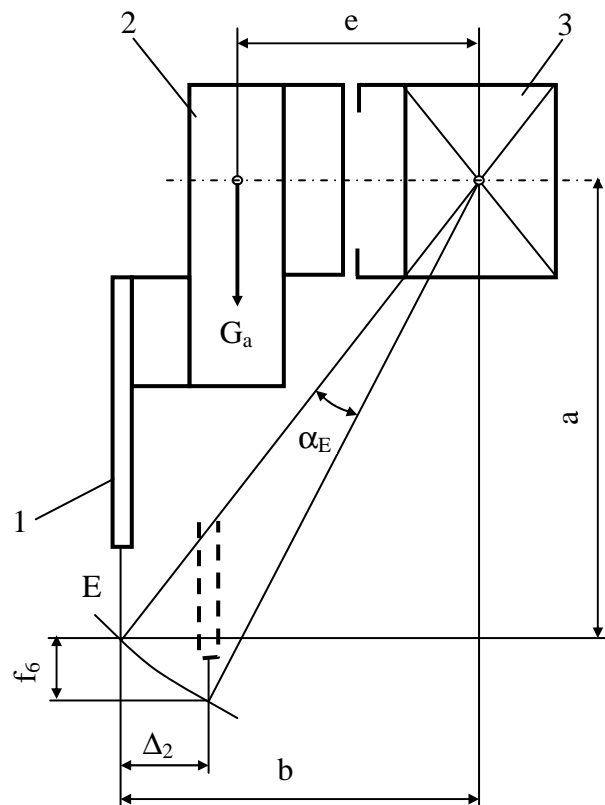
Розрахункова схема закрутки балки мостового візка: 1 - електрод; 2 - зварювальний автомат; 3 - балка з напрямними для автомата.
